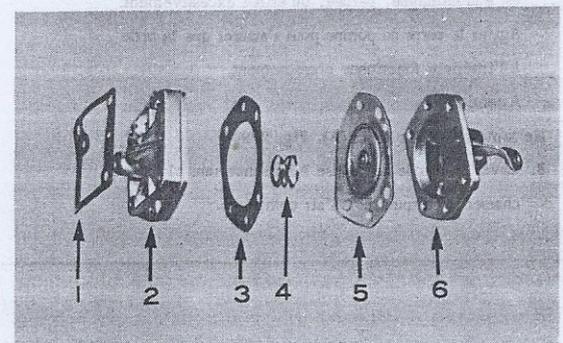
Assemblage de la membrane de pompe diaccélération
